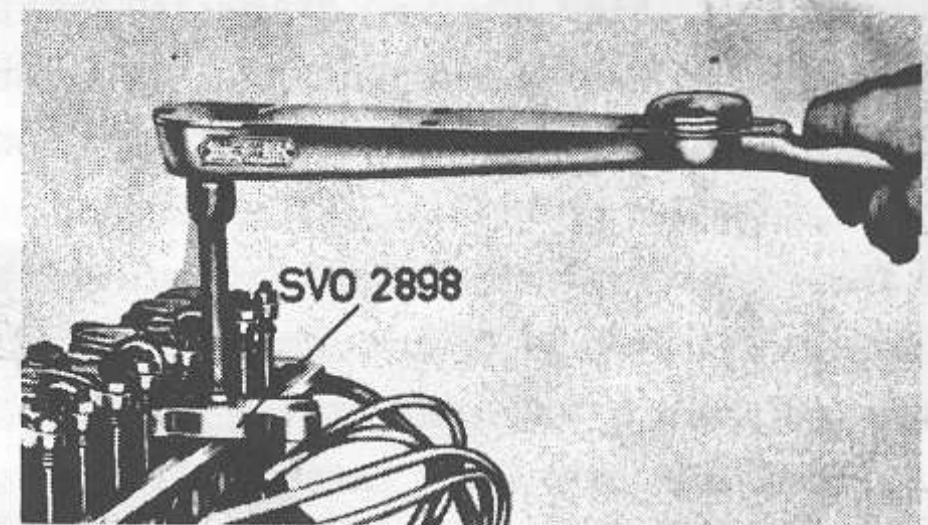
SVO 2898 Nyckel 11/16" för efterdragning av cylinderlocksskruvar
